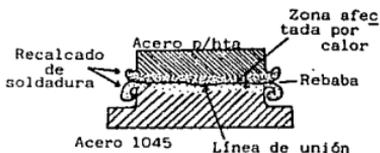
Sección transversal a través de una soldadura por fricción uniendo dos aceros disímiles.
